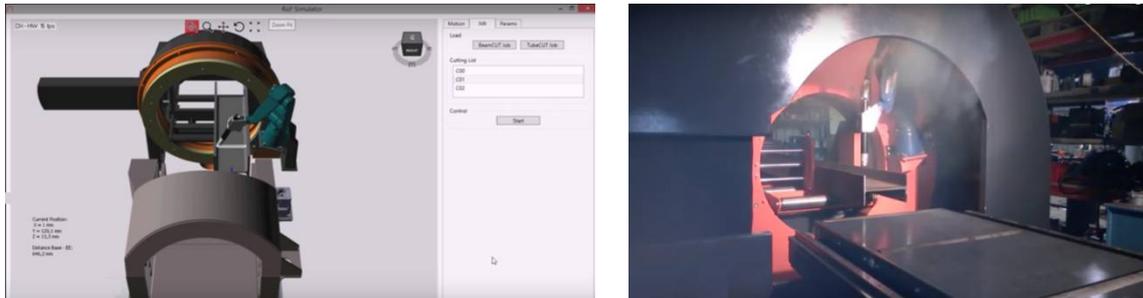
Célula de Soldadura de tubos e vigas SARKKIS Robotics
